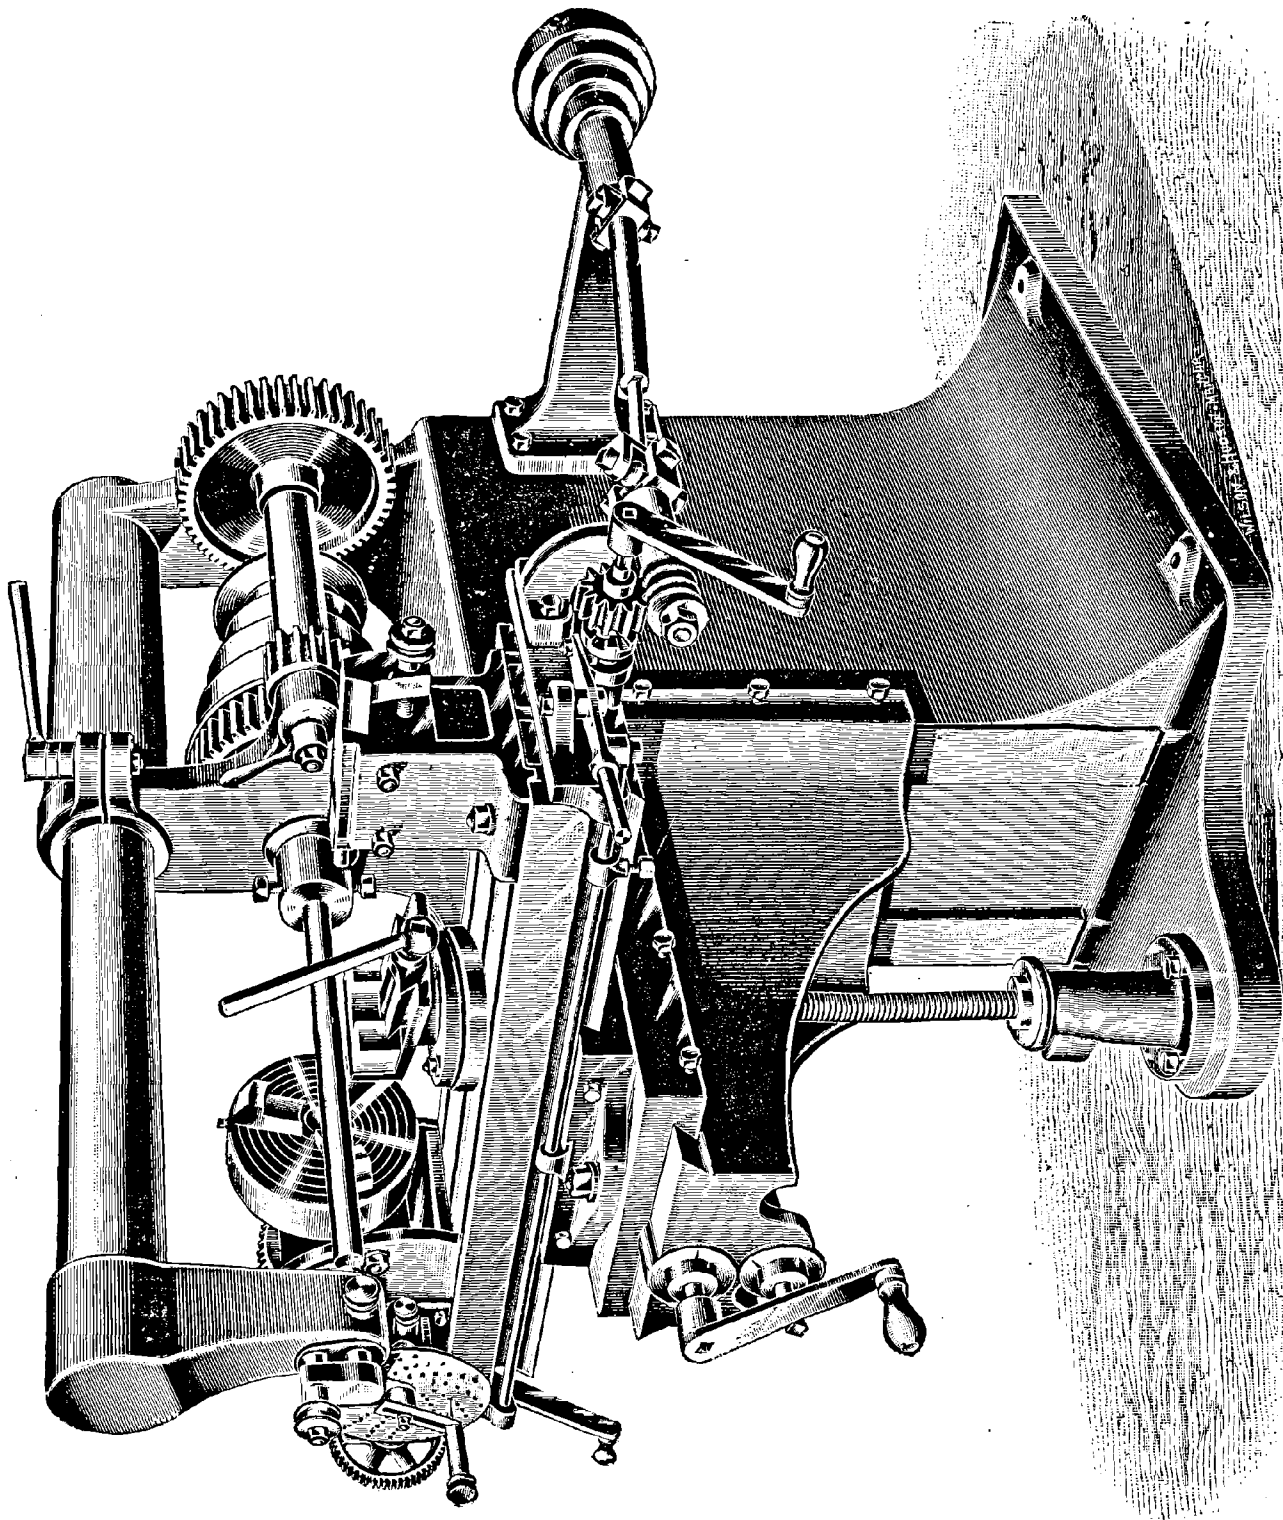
Machine à fraiser horizontale de M. Lucas.
